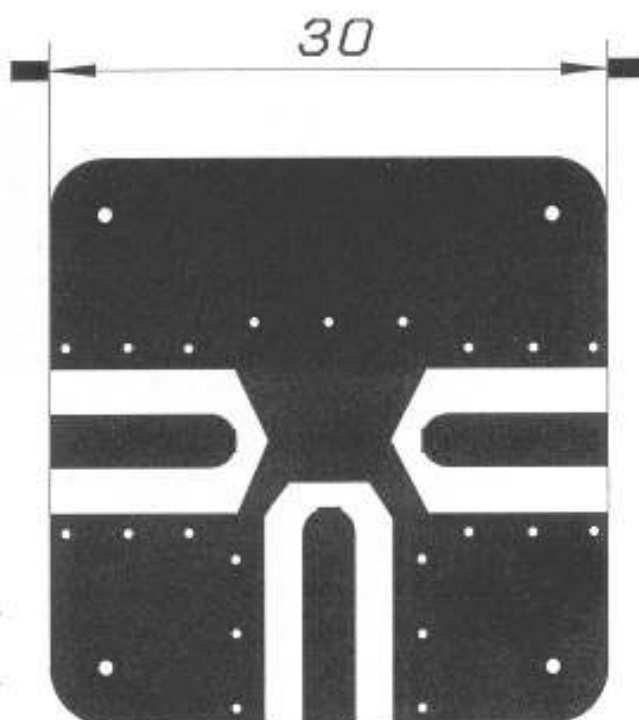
Platinen-Layout für Mischer-Versuchsaufbau
